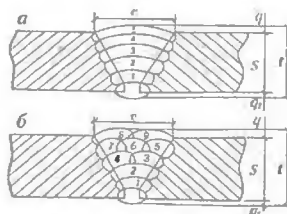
Зварювання багатшарових і багатпрохідних швів із зворотним підварюванням кореня:
